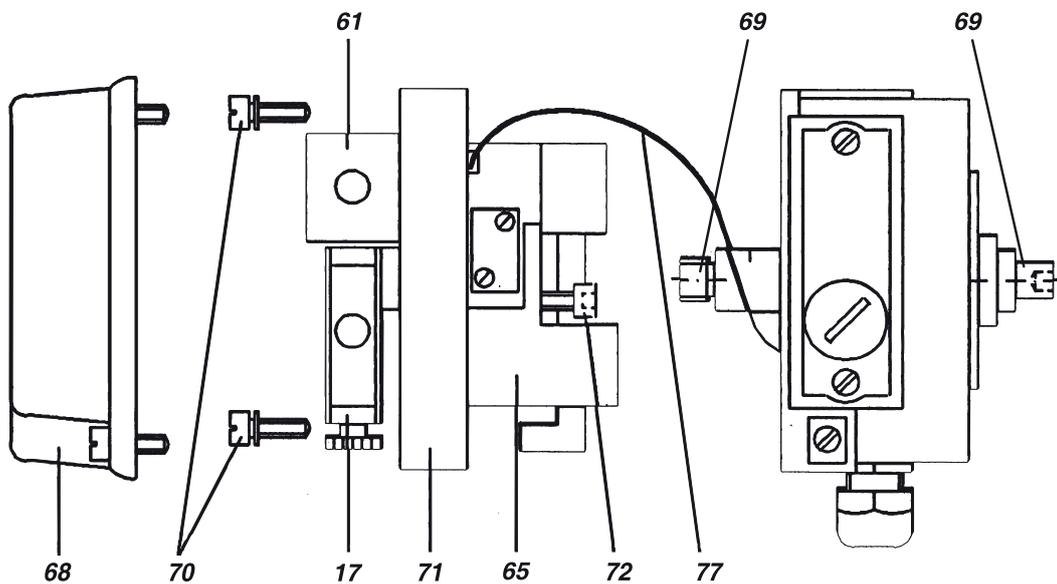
Remoção e remontagem do conversor I-p 65 e do amplificador 61
